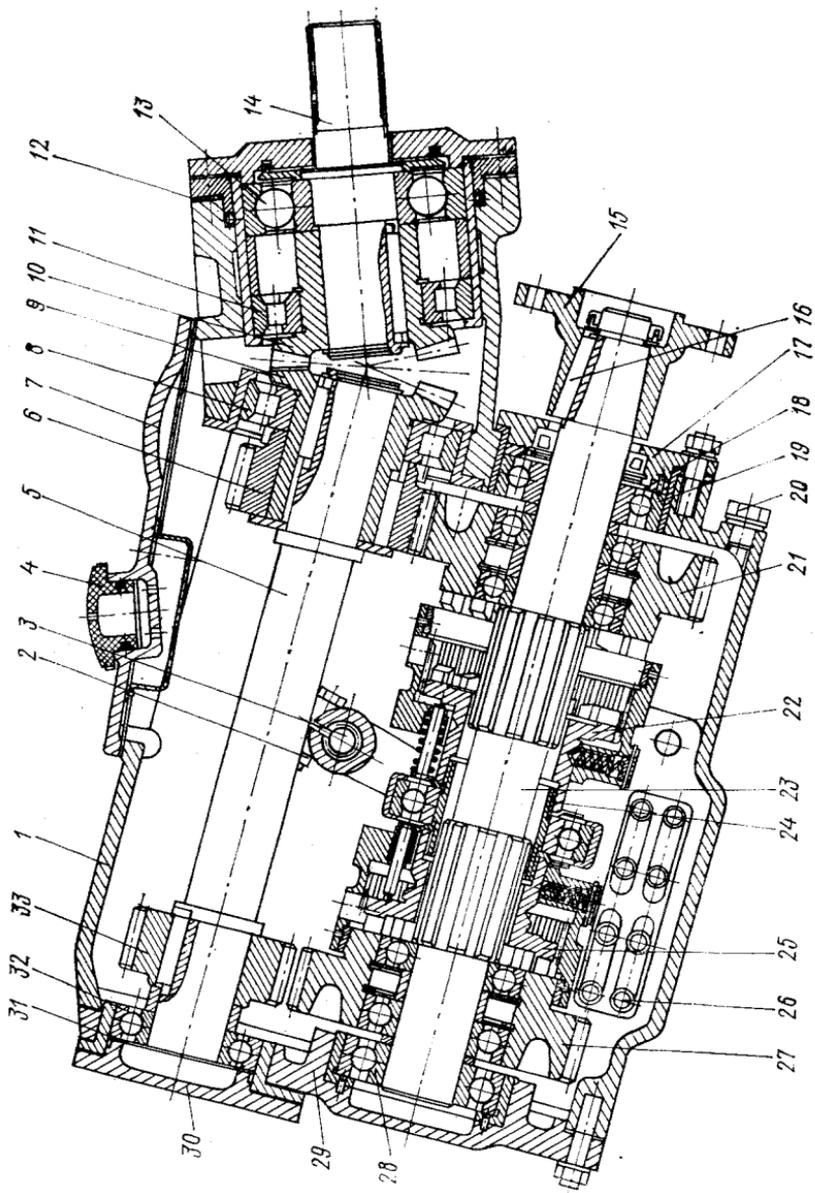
Продольный разрез реверсредуктора УРРП-25.
